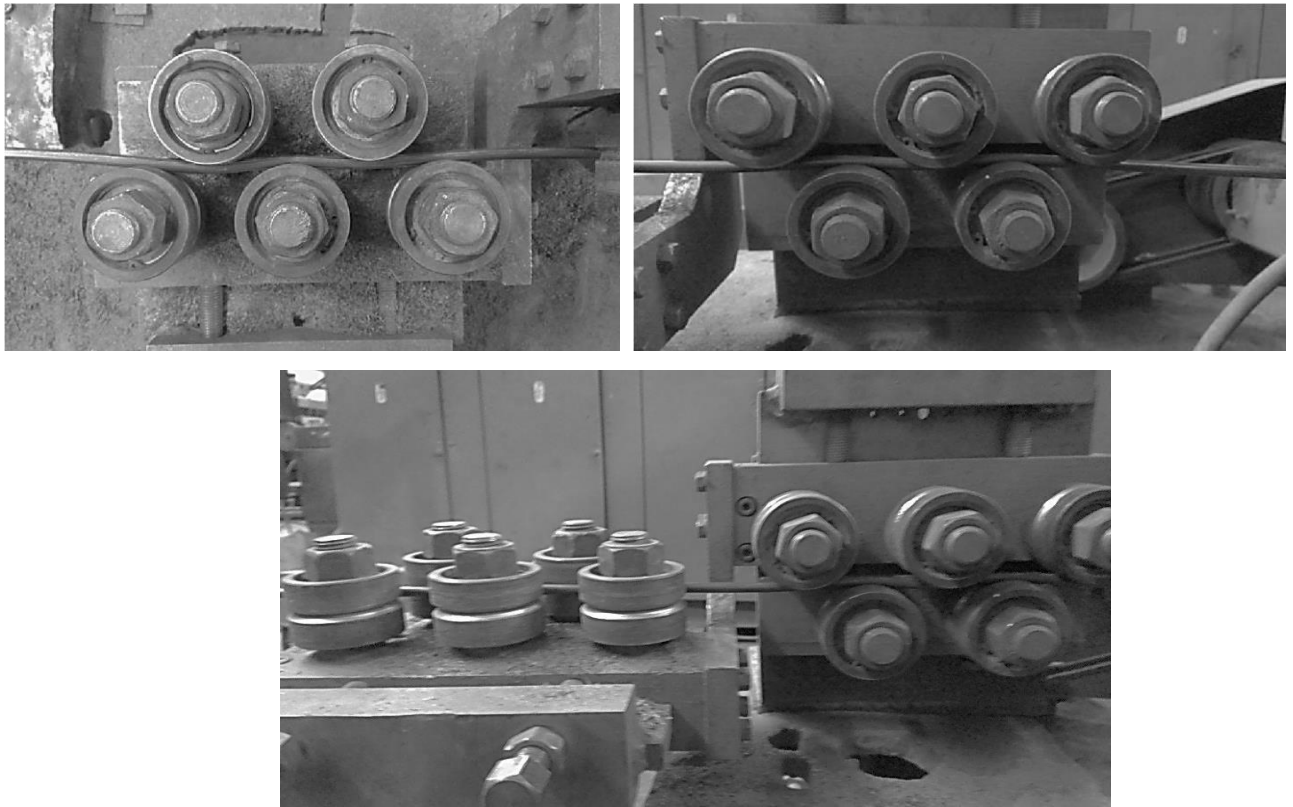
Пристрій для механо-циклічної обробки каліброваної заготовки $\varnothing 7,44$ мм
